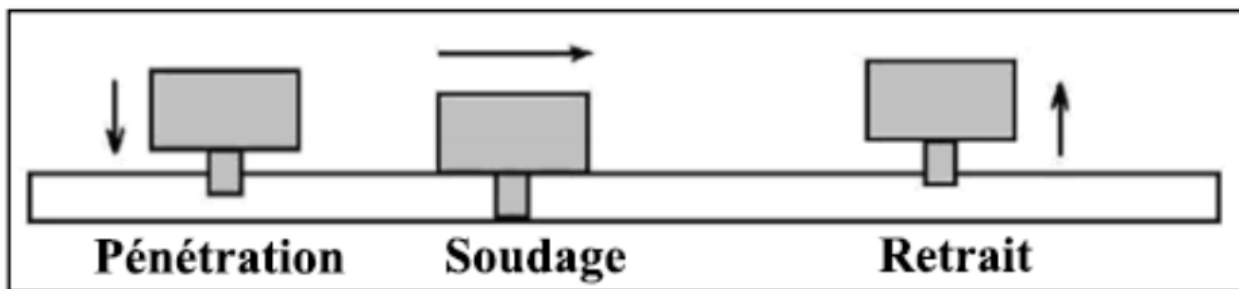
Etapes du Soudage bout à bout.
